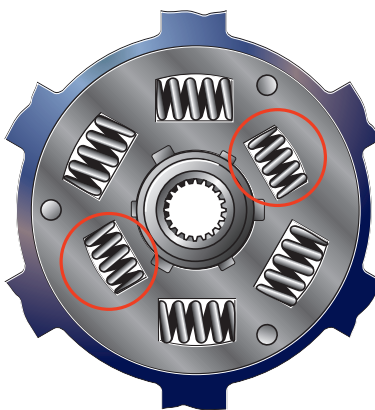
Две пружины из шести на диске нового поколения – меньшего размера и смещены ближе к центру.
